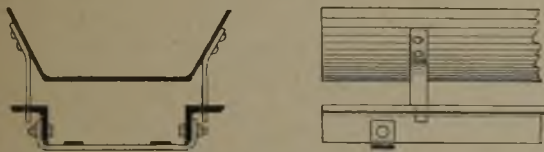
Querschnitt und Ansicht der Rinne des Blackett-Conveyors.
